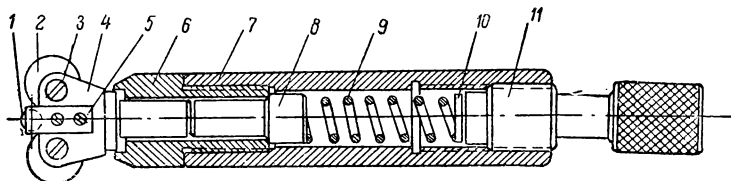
Державка с подпружиненным шариком для обкатывания поверхностей.
